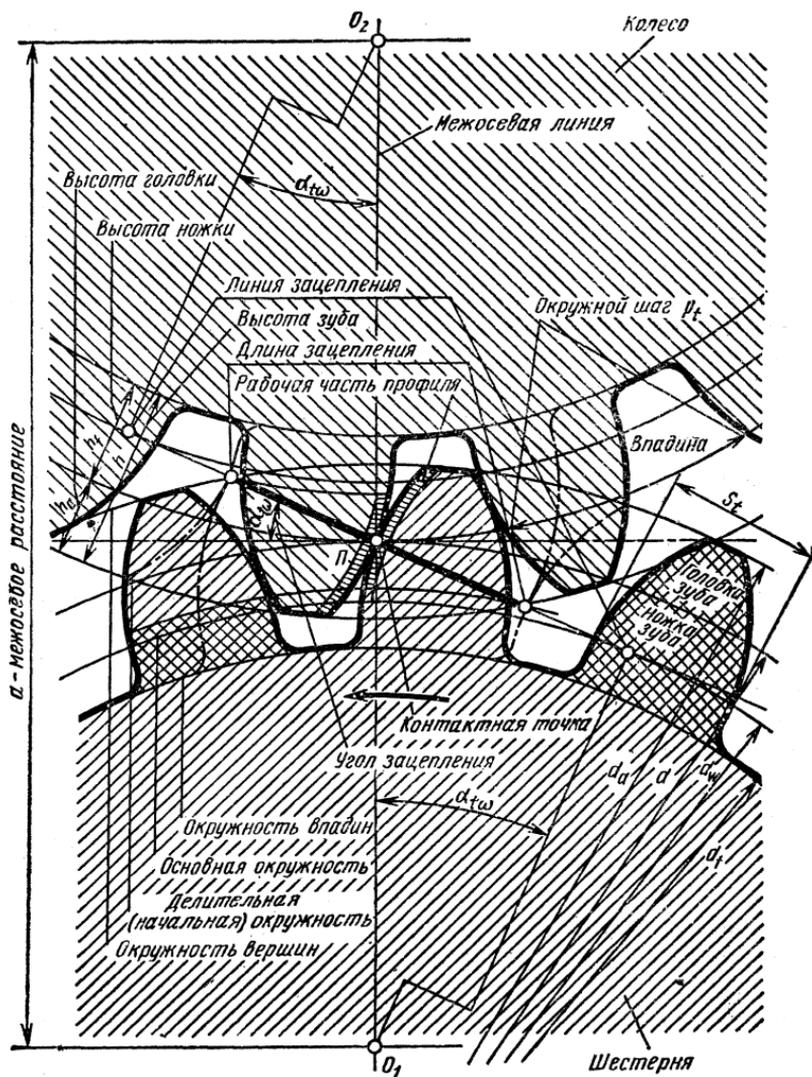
Элементы зубчатых колес и зубчатого зацепления
